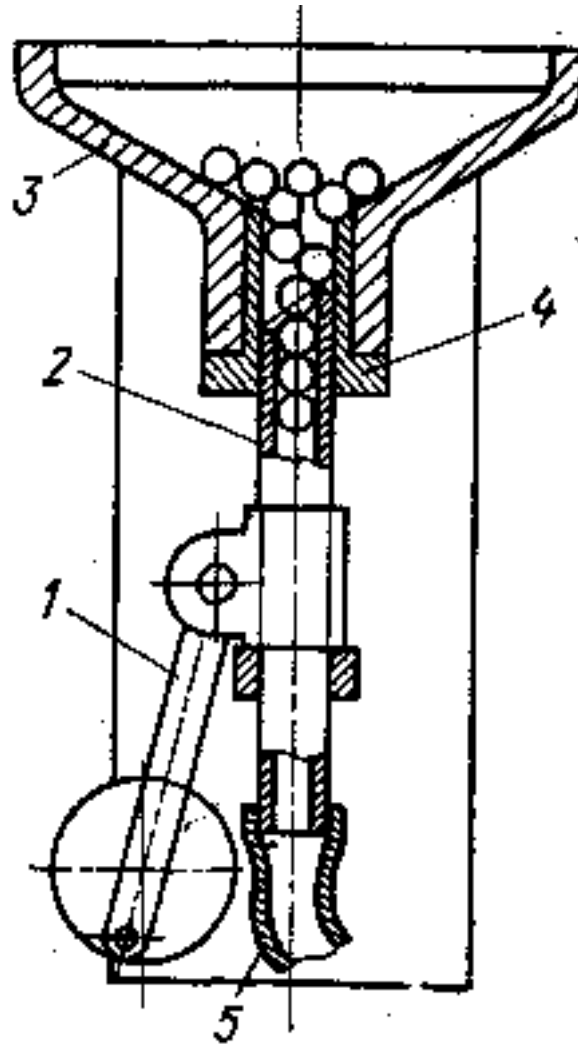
Бункер с подвижным трубчатым захватом деталей
